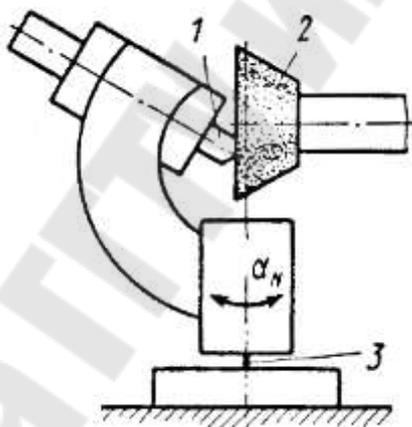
Приспособления для двухплоскостной заточки сверла: 1 – сверло; 2 – круг; 3 – ось поворота.
